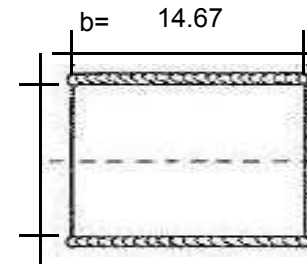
Detalle de la Soldadura en Bordos Superior e Inferior [ 13 ]
